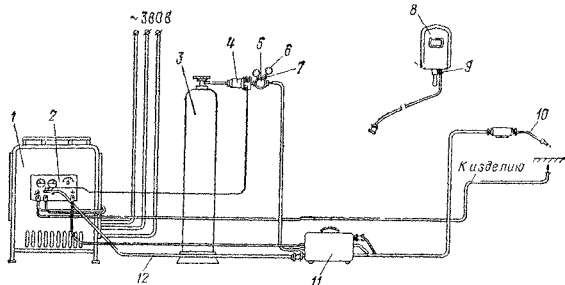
Полуавтоматическая установка А-547У для сварки тонкой электродами в среде углекислого газа
